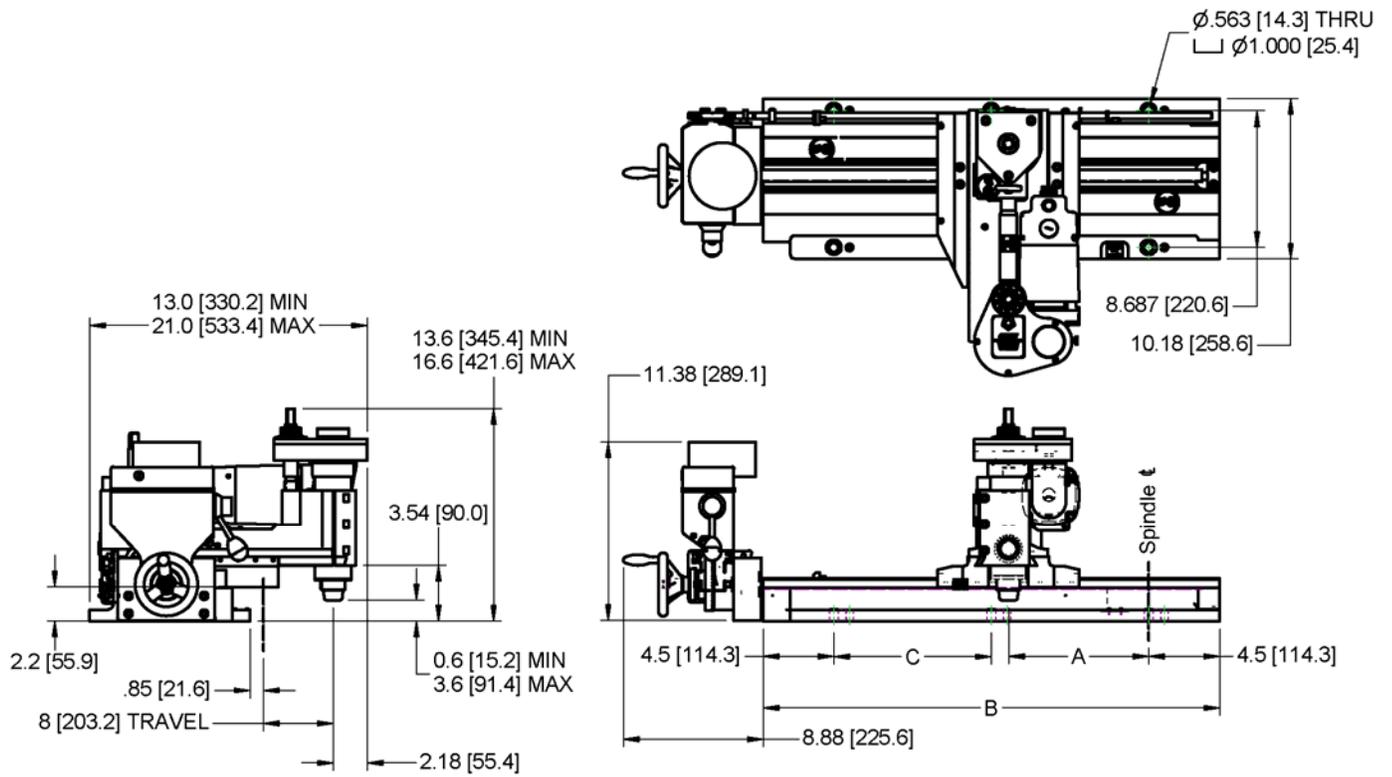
DIMENSIONES PARA HUSO WELDON (PULGADAS Y MILÍMETROS)
